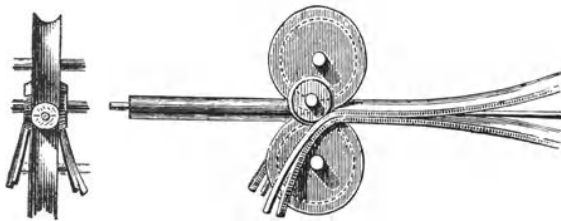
Maschine zur Bedeckung von Drähten mit einer Kautschukhülle.
